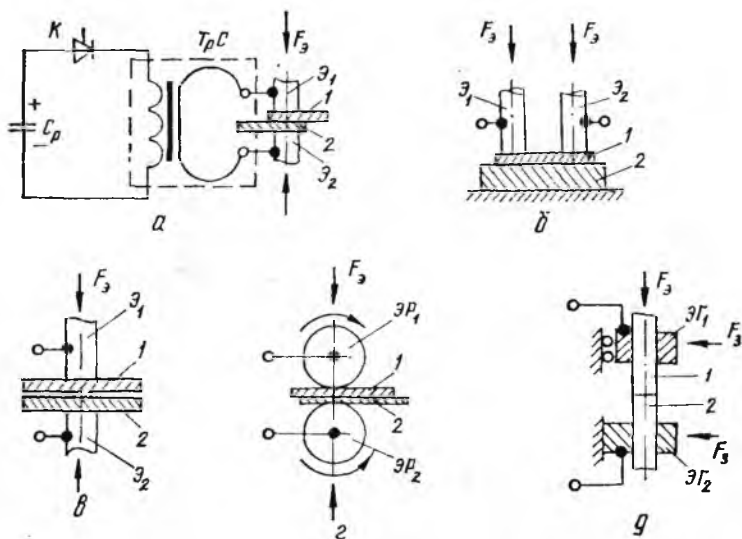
Схемы трансформаторной конденсаторной сварки сопротивлением: а — точечная двусторонняя; б — точечная односторонняя; в — рельсно-точечная; г — шовная; д — стыковая.
